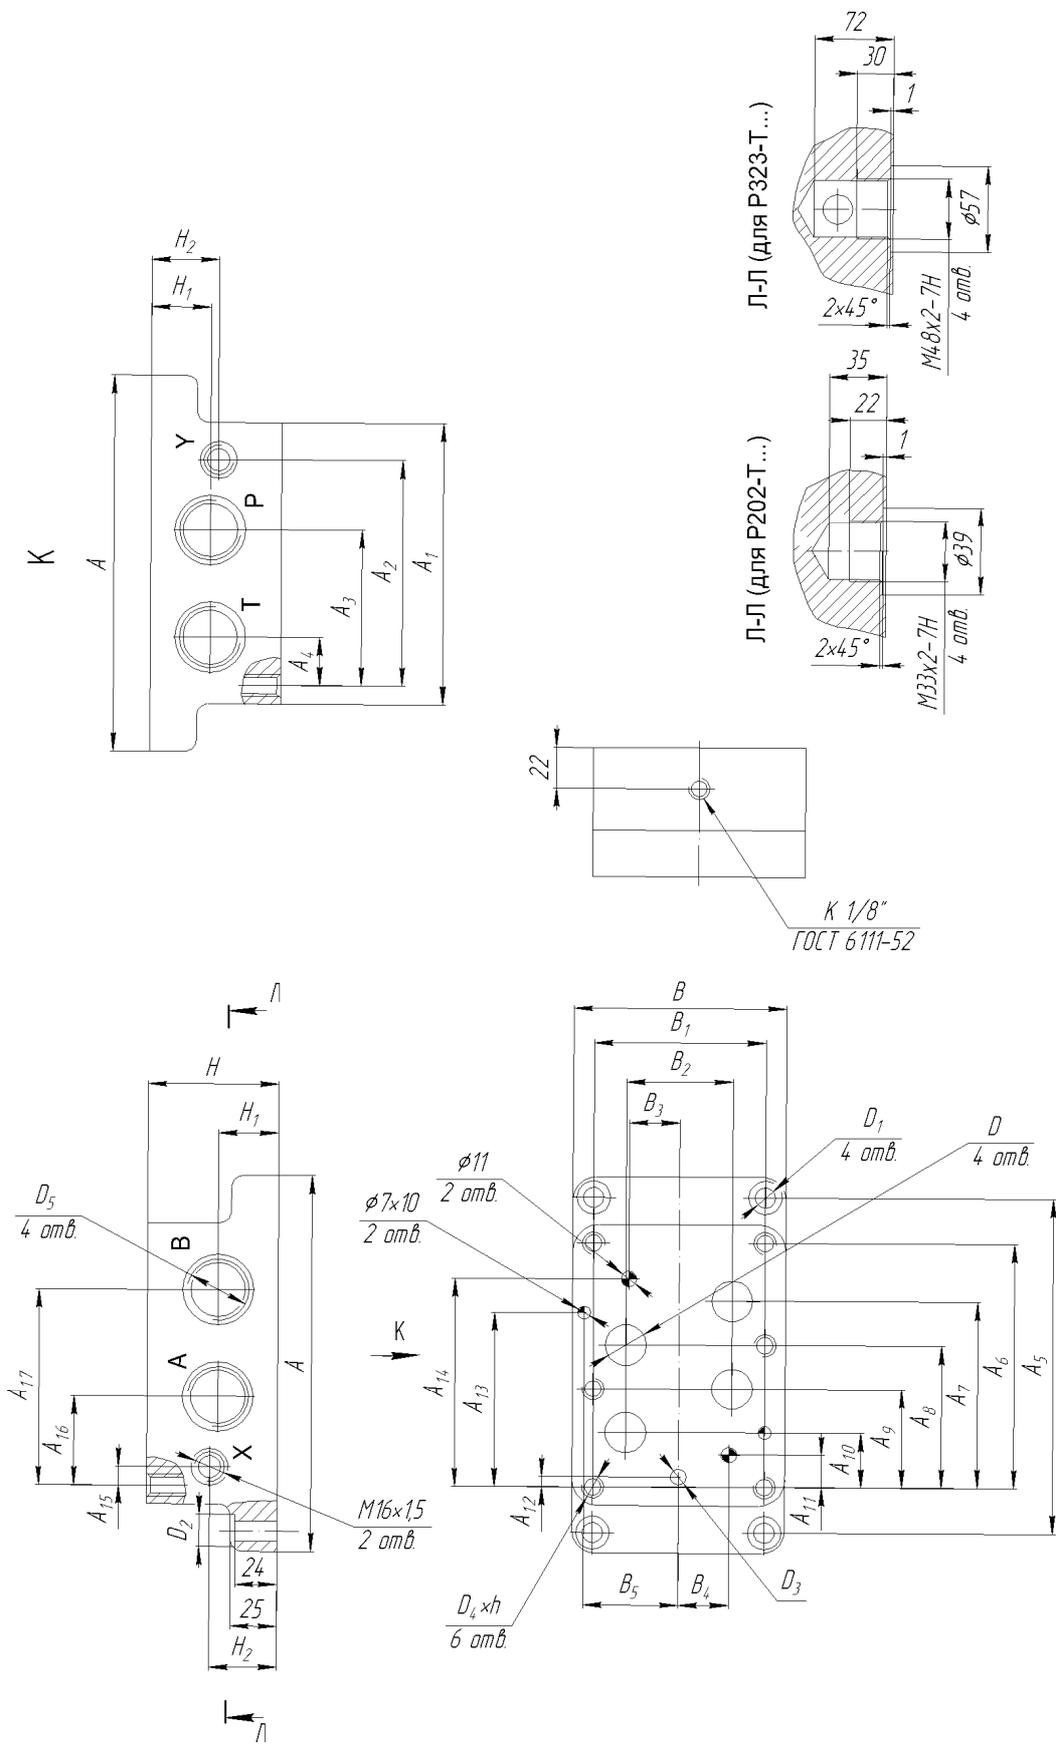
Габаритные и присоединительные размеры присоединительных плит.
